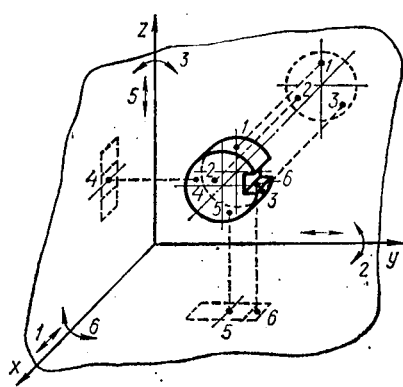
Схема базирования цилиндрической заготовки с соотношением $\frac{l}{d} < 1$
